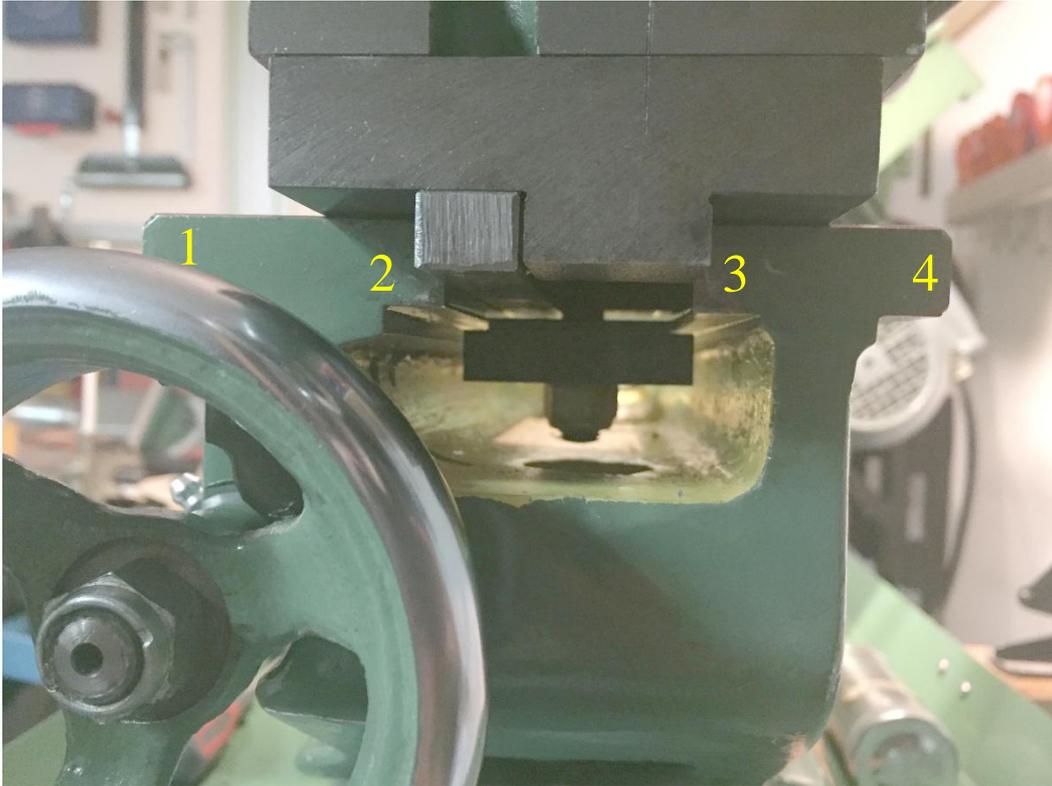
Aufbau des Maschinenbettes und die 4 Führungsflächen
